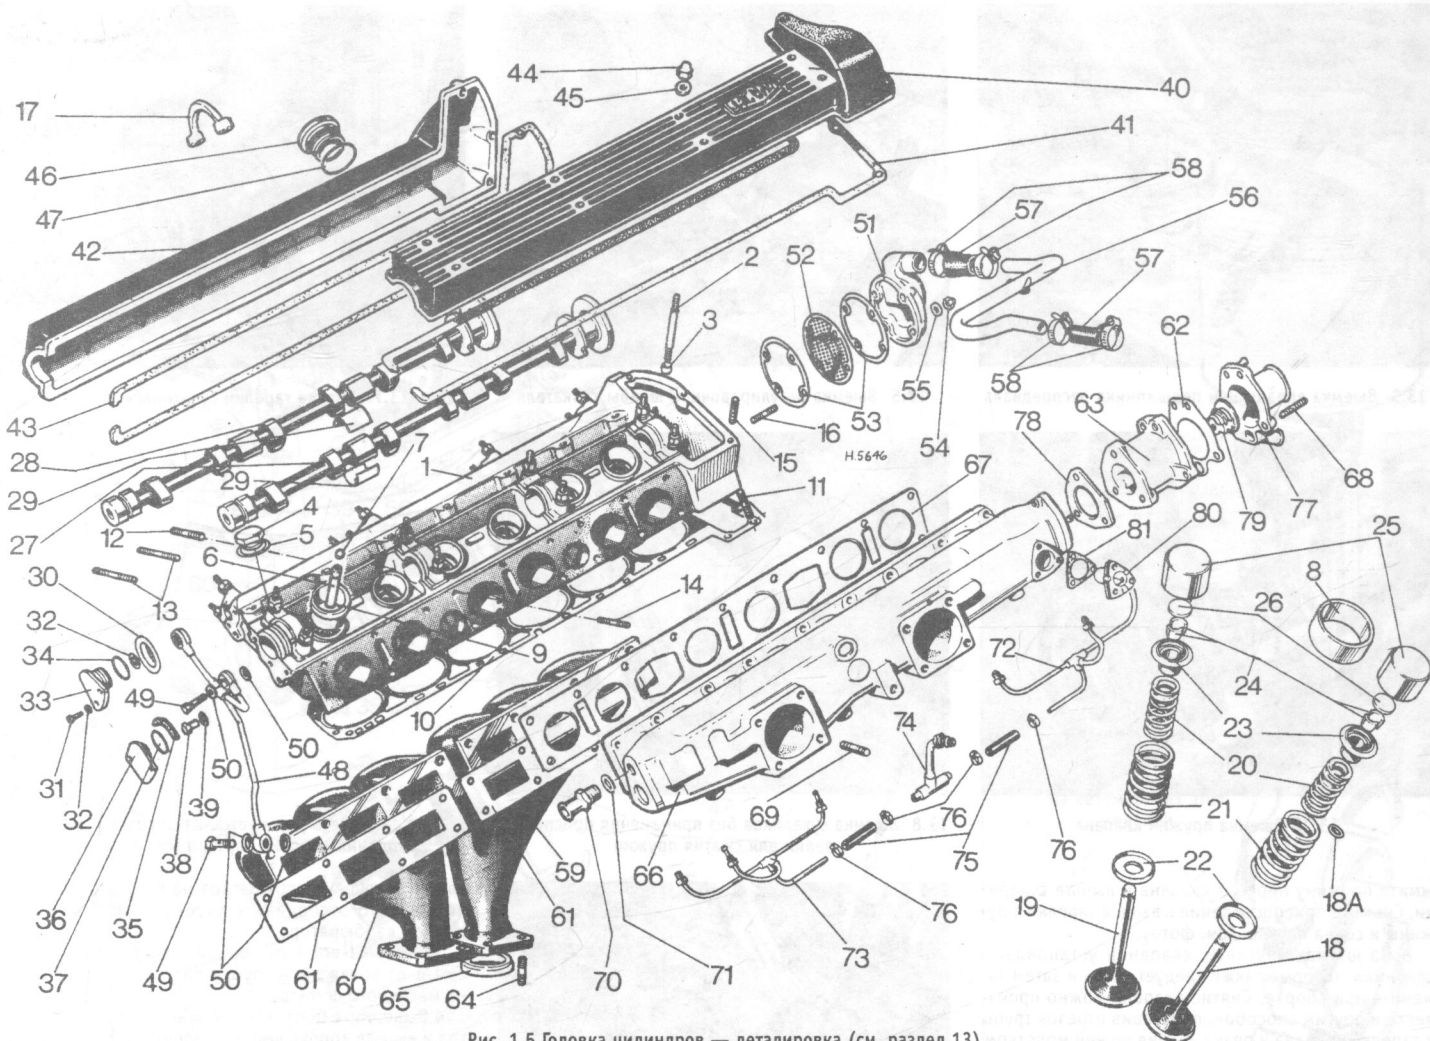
Головка цилиндров — деталировка (см. раздел 13)
